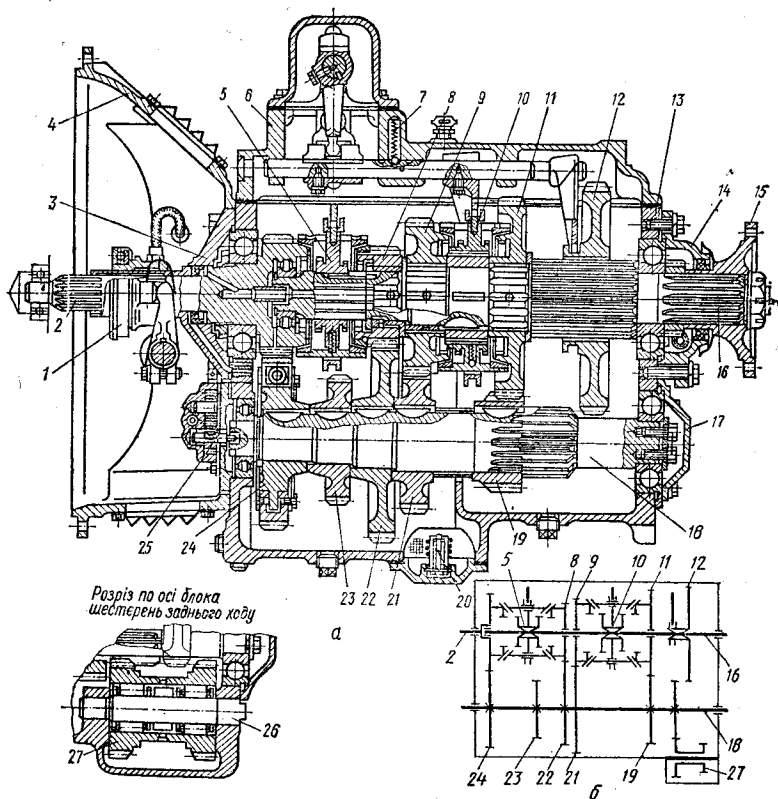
Коробка передач автомобіля МАЗ-5335:
